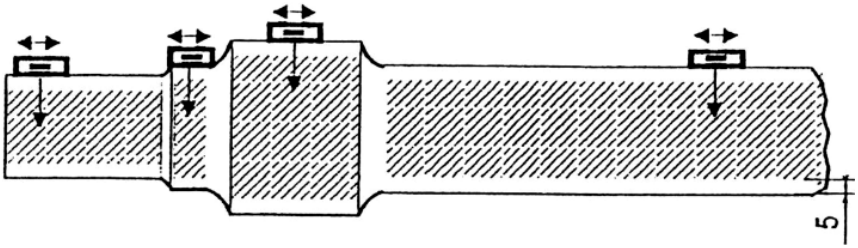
Схема контроля при вводе ультразвука прямым ПЭП с цилиндрической поверхности чистовой оси колесной пары
